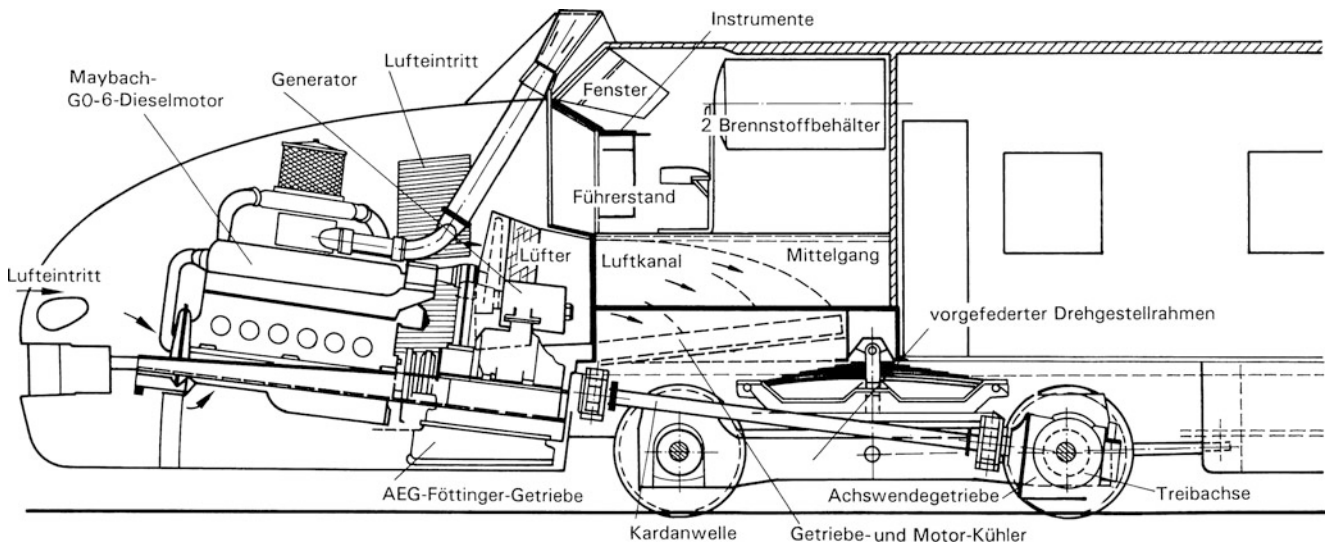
Im Kruckenberg-Schnelltriebwagen waren der Dieselmotor und das angeflanschte hydraulische Getriebe im Fahrzeugaufbau gelagert
